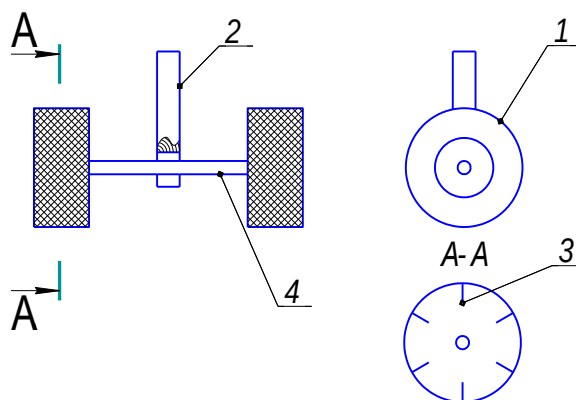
Дополнительная конструкция сушилки барабанного типа:
